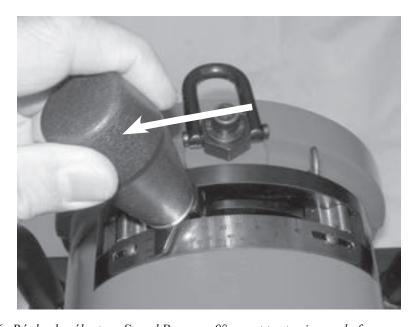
Réglez le sélecteur Speed Prep sur 0° avant tout usinage de forme.
